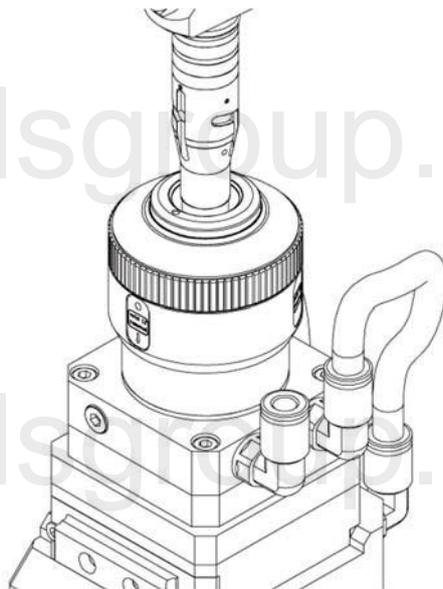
Установка: Волоконный лазерный источник (соединитель типа QВН)
